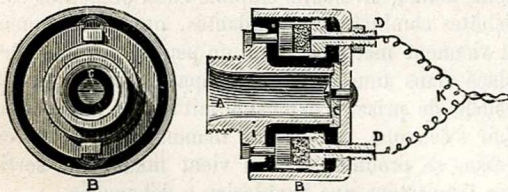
Ouverture d'une bouche par combustion d'un fil.
